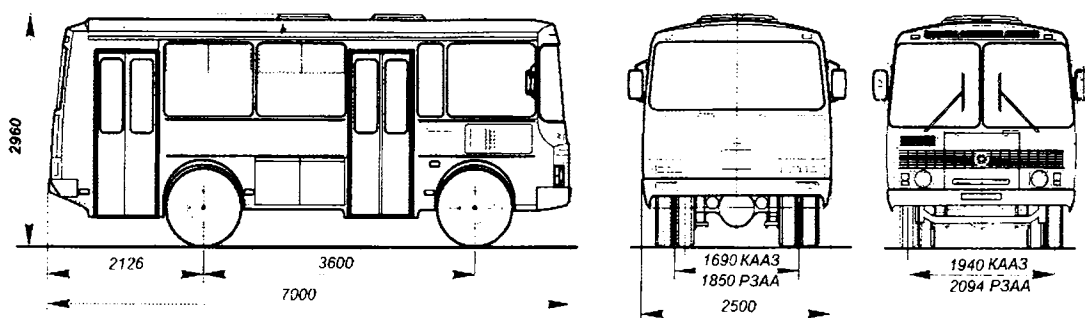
Габаритные размеры автобуса ПАЗ-32053.
